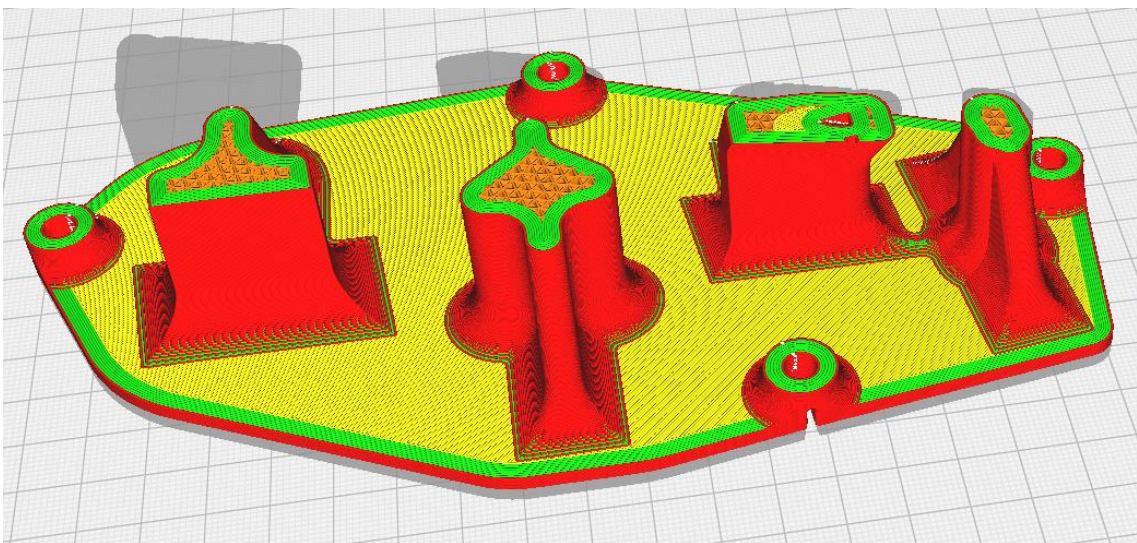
Vista módulo 2 del utillaje para pieza 1 en el laminador de Ultimaker Cura
